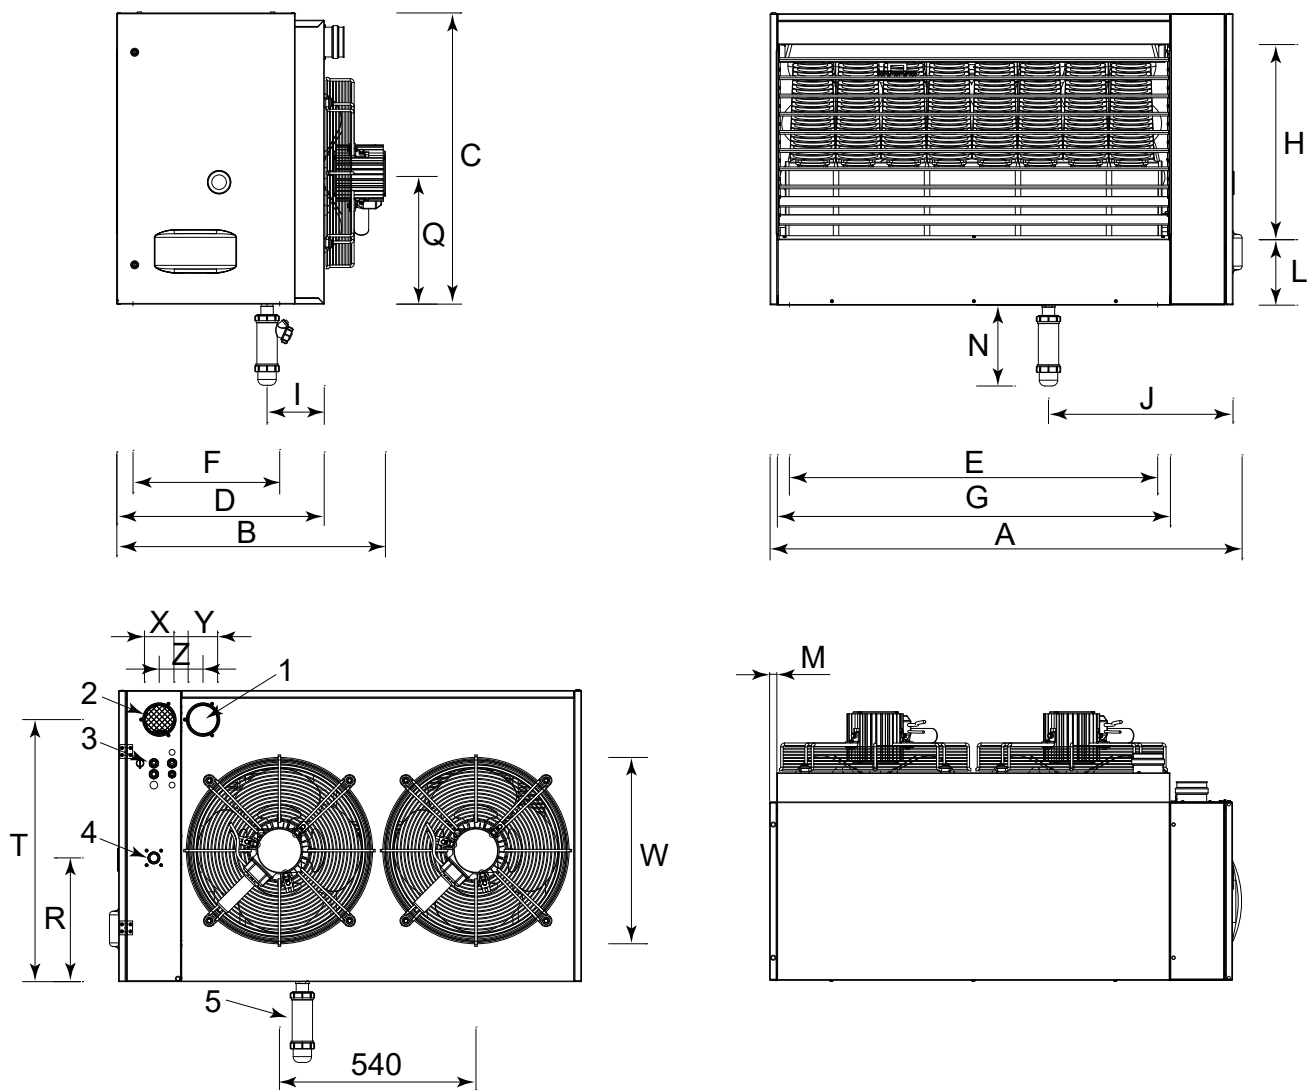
Габариты воздухонагревателей G30, G45, G60
